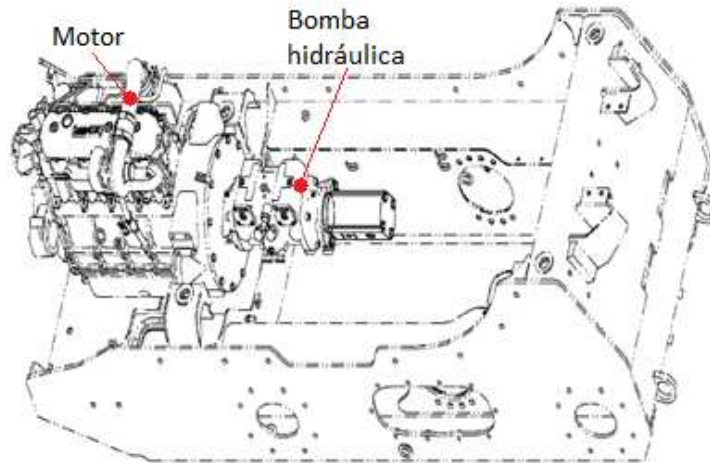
Partes del Bastidor Minicargadora<sup>90</sup>
